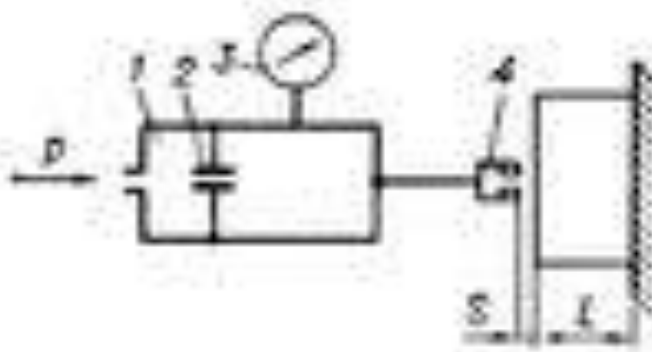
Пневматичний вимірювальний прилад манометричного типу:
